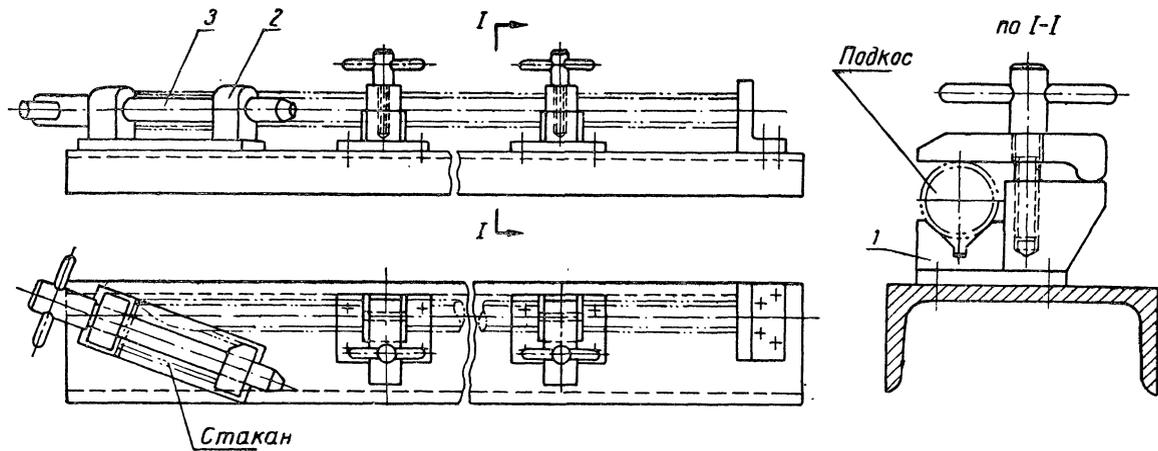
Приспособление для сборки и прихватки кронштейна.
